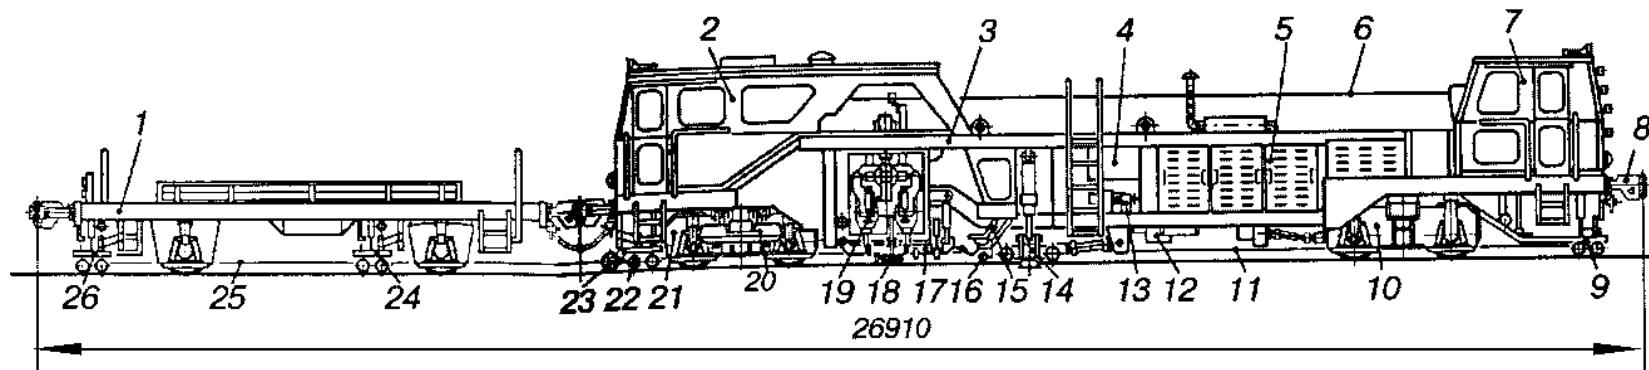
Выправочно-подбивочно-рихтовочная машина для стрелок и пути ВПРС-500: 1 – полуприцепная платформа; 2 – дополнительный топливный бак; 3, 7, 14 – кабины машиниста, оператора и рабочая; 4 – рама; 5 – дизельная силовая установка; 6 – тросы нивелировочно-измерительной системы; 8 – автосцепки; 9, 20, 23 – передняя, контрольно-измерительная и задняя тележки КИС; 10 – мерный каток с датчиком пройденного пути; 11, 18 – тяговая и бегунковая тележки; 12 – силовая передача (трансмиссия); 13 – трос-хорда рихтовочной КИС; 15 – ПРУ; 16 – нивелировочно-рихтовочное измерительное устройство КИС; 17 – одношпальные подбивочные блоки; 19 – уплотнители балласта у торцов шпал; 21 – опора платформы; 22 – колёсная пара
